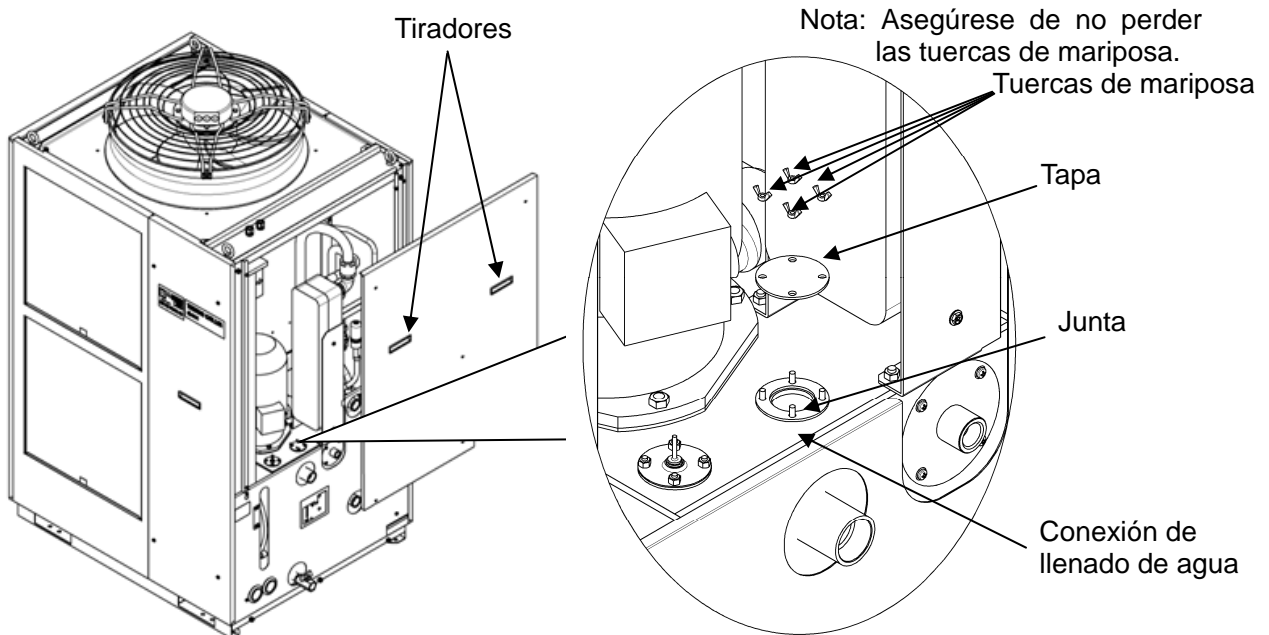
Retirada del panel derecho y la tapa de la conexión de llenado de agua
